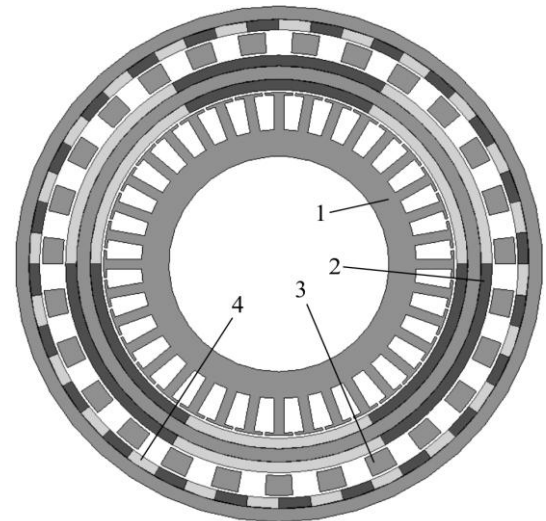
Общий вид электродвигателя с магнитным редуктором
